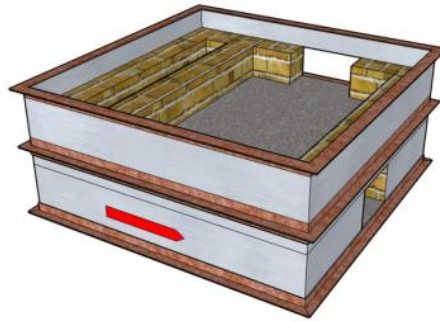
Módulo 2 ou cinzeiro com detalhes do revestimento interno com tijolos e montado sobre o módulo 1 ou câmara inferior.
